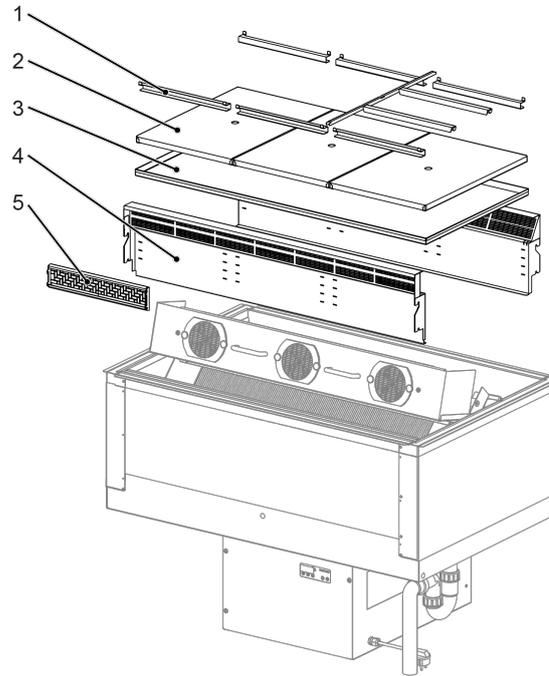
Bauteile zur Reinigung in der Spülmaschine
